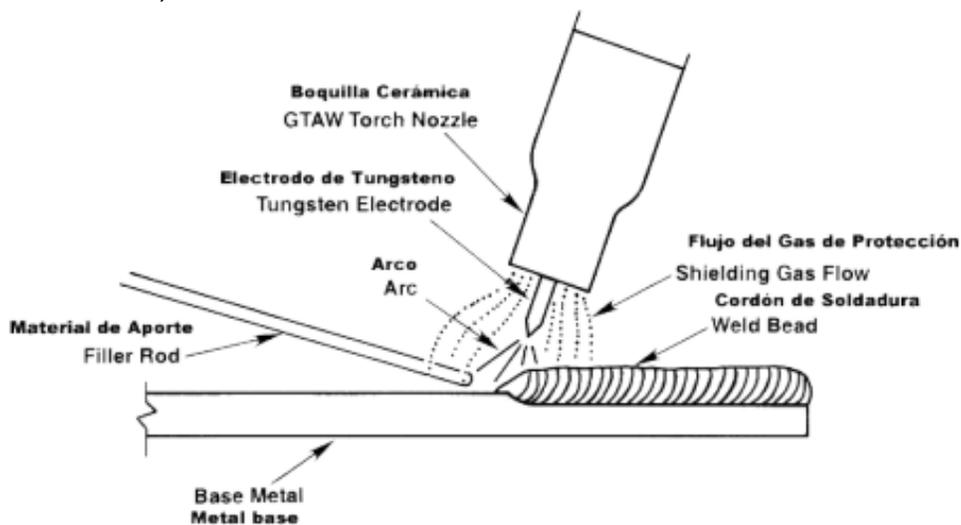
7 Funcionamiento de Soldadura TIG
